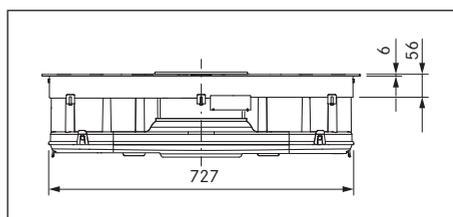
BHU dimensioni apparecchio vista frontale
